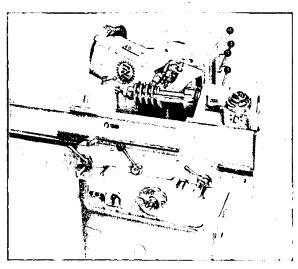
Schneckenfräsmaschine (Zahnradfabrik Zuffenhausen)
